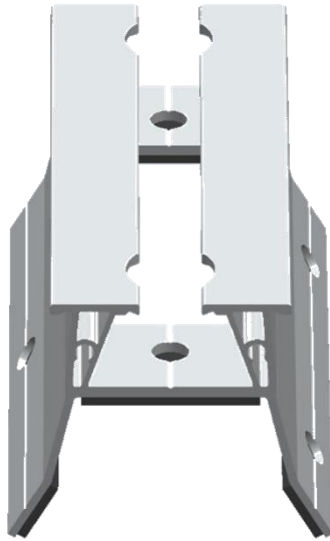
Profilé ISY-STEEL : vue d'ensemble
